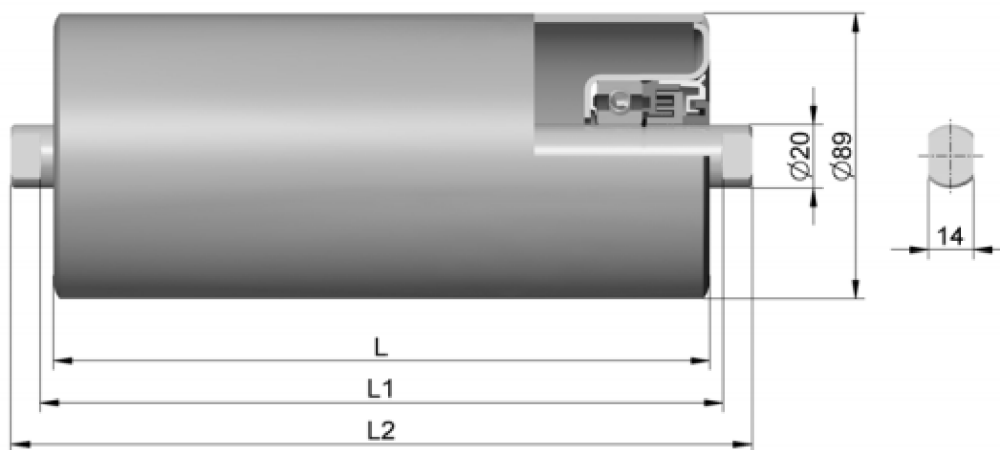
Držák spodního válečku DSV 650/Ø89/14 [18]
